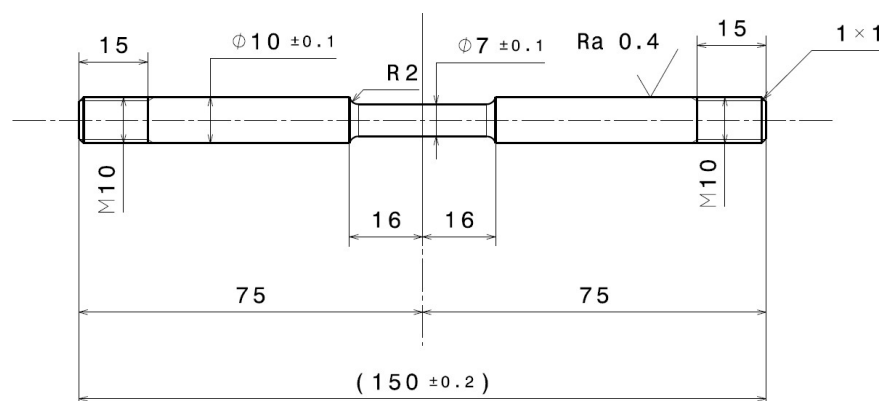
Géométrie d'éprouvette avec rétreint (dimensions en mm)
